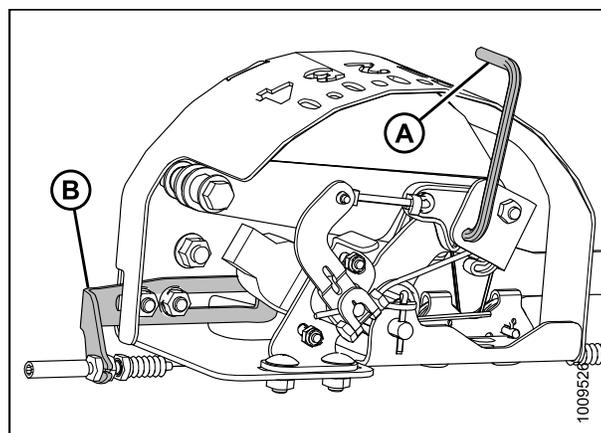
Ensemble de capteurs de hauteur automatique de plateforme de 10 volts
